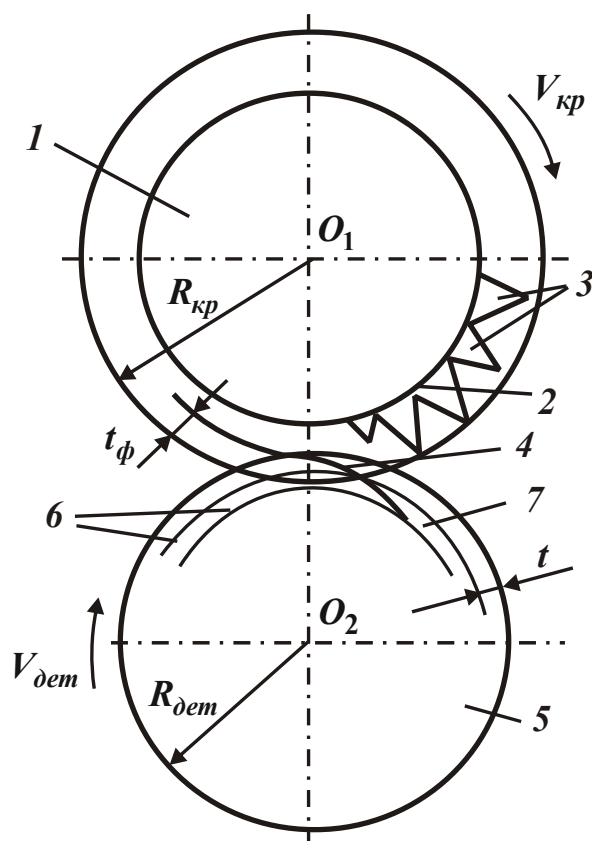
Расчетная схема круглого наружного шлифования: 1 – круг; 2 – уровень связки круга; 3 – режущие зерна; 4 – линия полного съема материала; 5 – деталь; 6 – элементарные цилиндрические оболочки, которыми представлен снимаемый припуск; 7 – слой остаточной шероховатости обработанной поверхности
